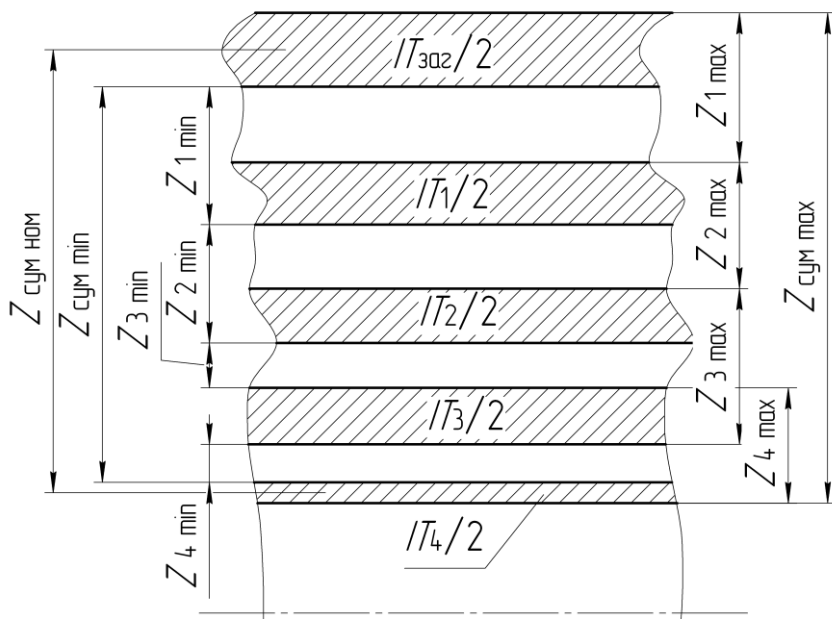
Схема розташування проміжних припусків і допусків на проміжні та початкові розміри заготовки при різних способах установки різального інструмента на розмір
